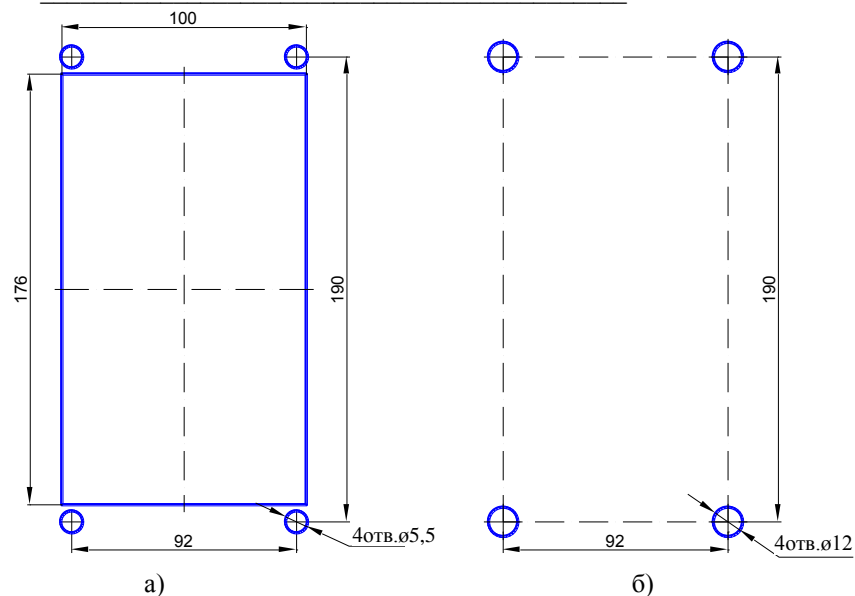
Разметка под крепление DP400-TDC22 а) снаружи; б) изнутри.
